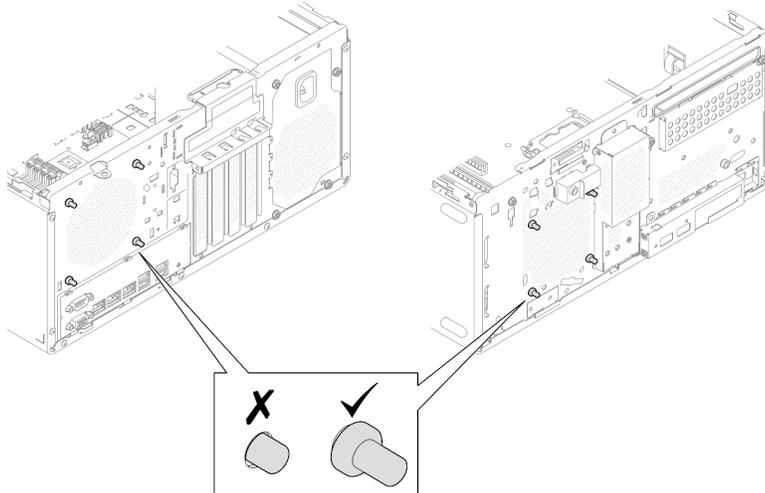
Installation des supports en caoutchouc du ventilateur avant et du ventilateur arrière
